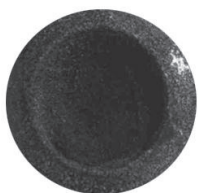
Поверхность отливки опытного образца, который оформлялся неокрашенной замороженной формой
